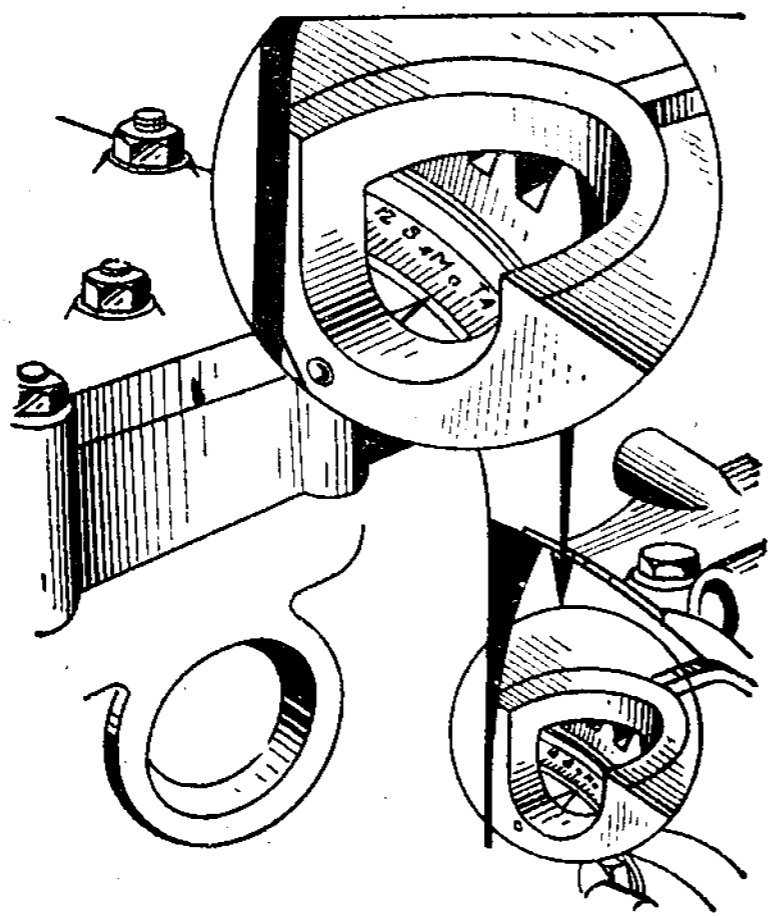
Установка поршня 1-го цилиндра в верхнюю мертвую точку
